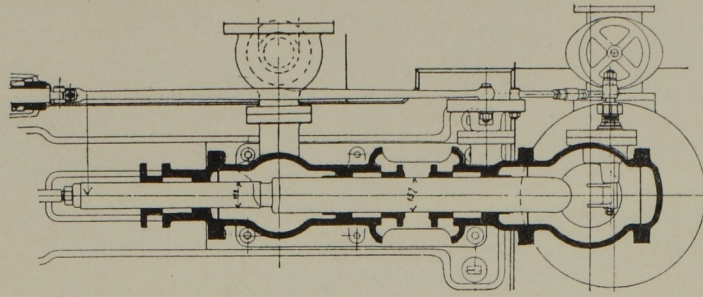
Grundriss der Pumpe mit Steuerung. Masst. 1:30.
